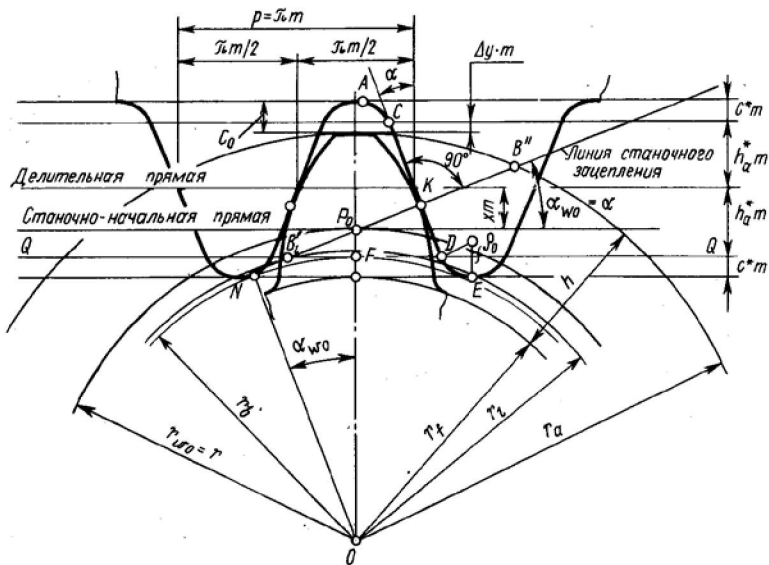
Основные параметры реечного инструмента и зубчатого колеса
